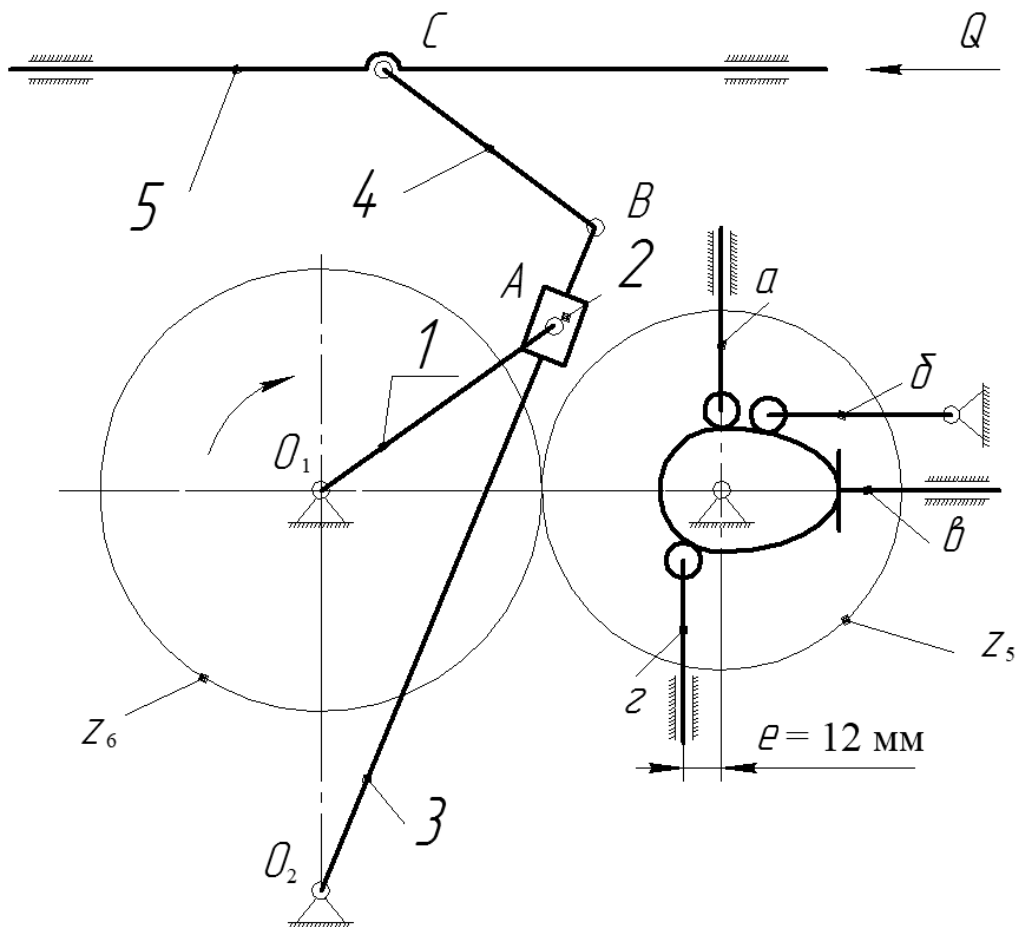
Кинематическая схема механизма поперечно-строгального станка
